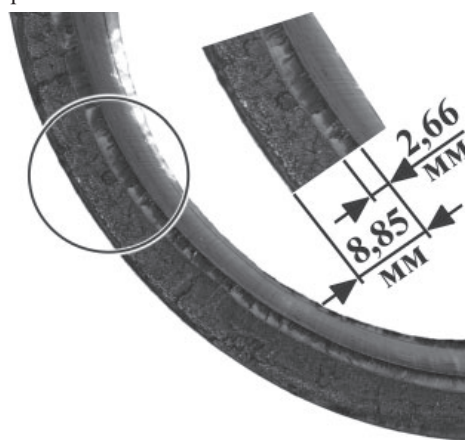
Размеры кольцевой трещины в подгратовой зоне сварного шва.
